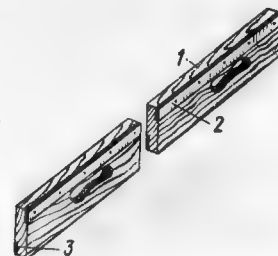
1 — рейка; 2 — пластина верхняя; 3 — пластина нижняя
